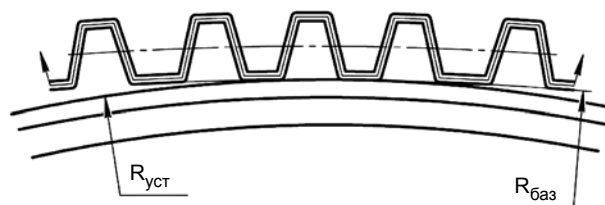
Схема частичного упругого восстановления зубчатого сектора после снятия формообразующих воздействий
